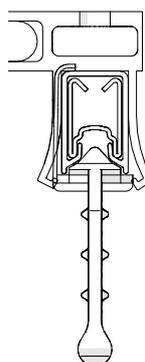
Demontage-Werkzeug in der Anwendung (vorne)
